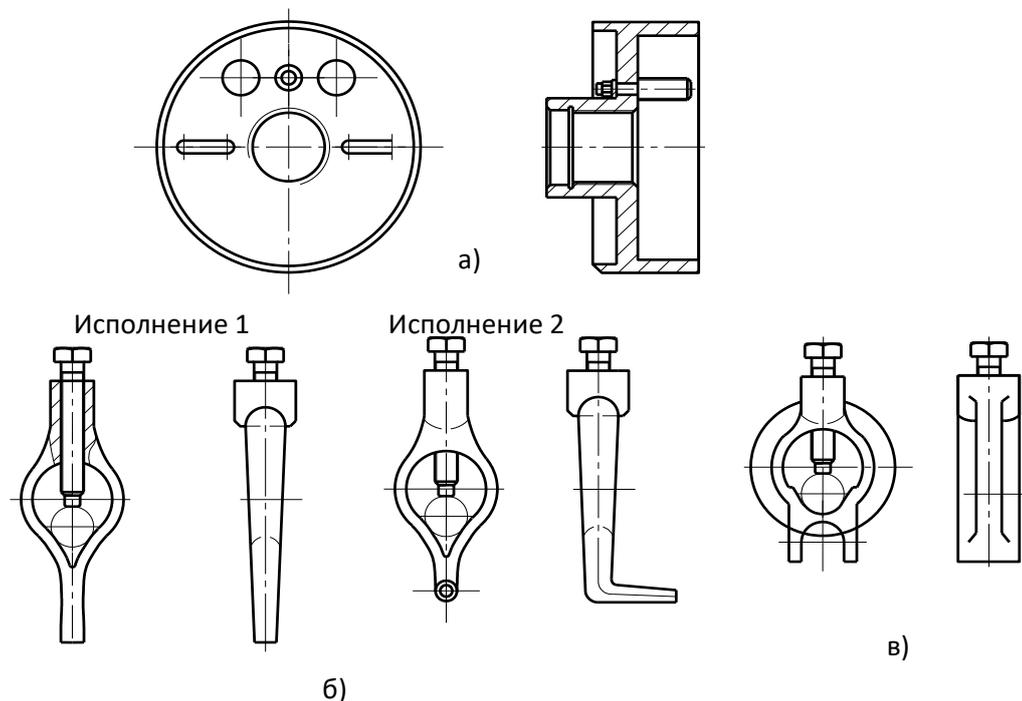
Поводковый патрон (а) и хомутики для токарных и фрезерных работ (б – для токарных станков; в – для фрезерных станков)
